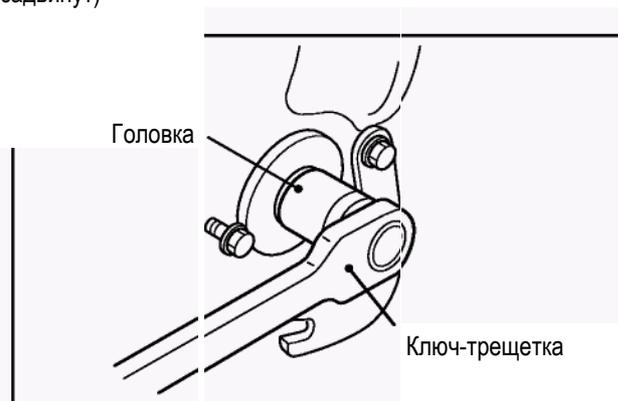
Положение валоповоротного устройства (Проворачивание вала)
